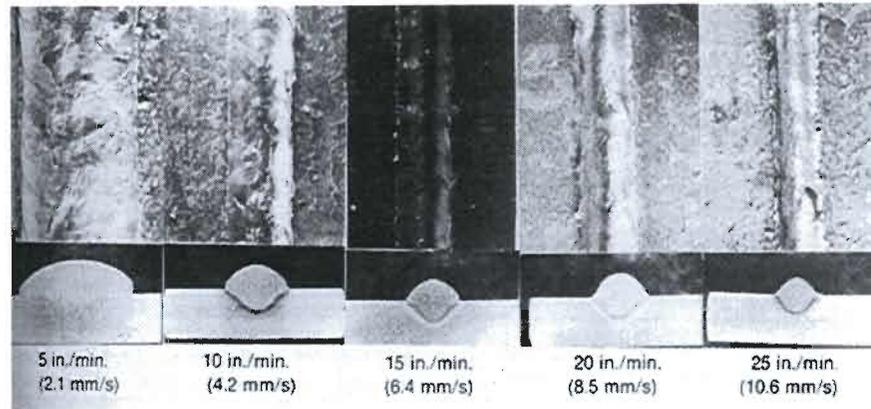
Efecto de la velocidad en la apariencia del cordón, condiciones de soldadura: corriente 175 amp voltaje 21, tamaño del electrodo 0.035" gas CO2 stick out de 3/8"
